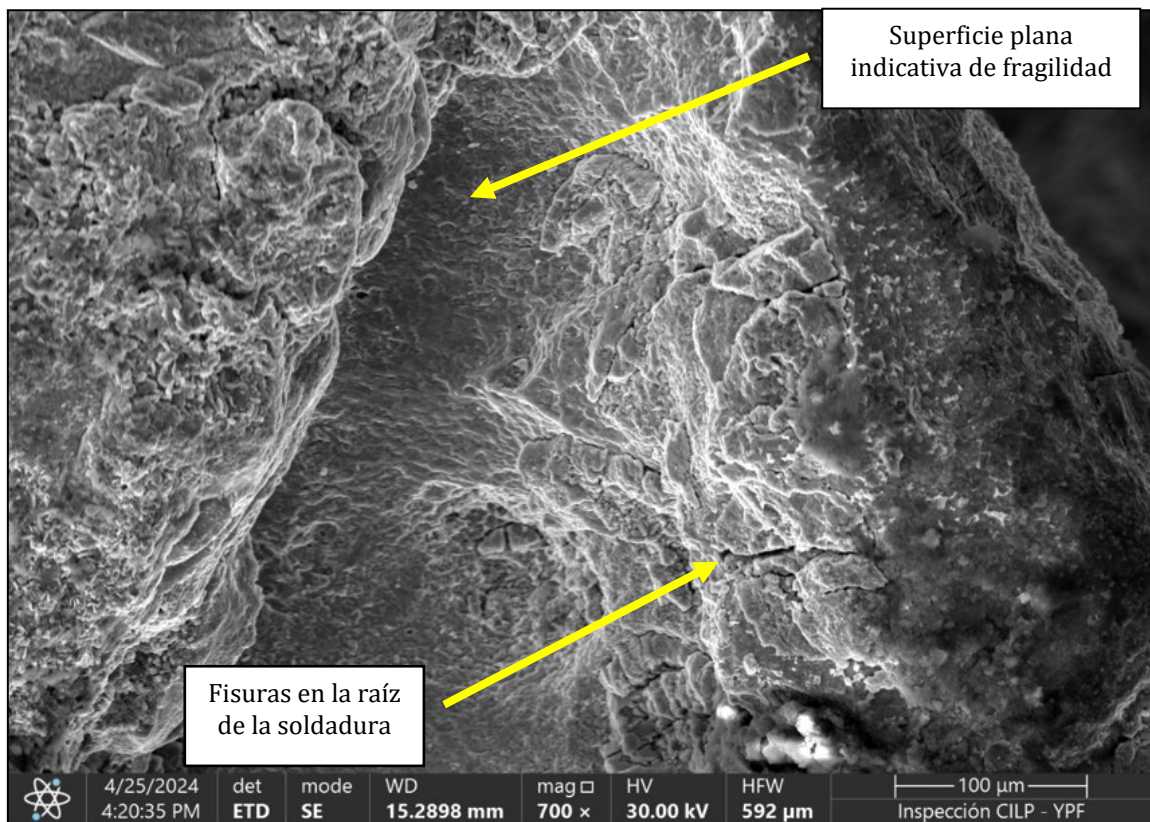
Superficie de fractura – Codo superior – Cordón circunferencial. Se observan fisuras que inician en la raíz de la soldadura, así como también, una superficie de fractura frágil.
